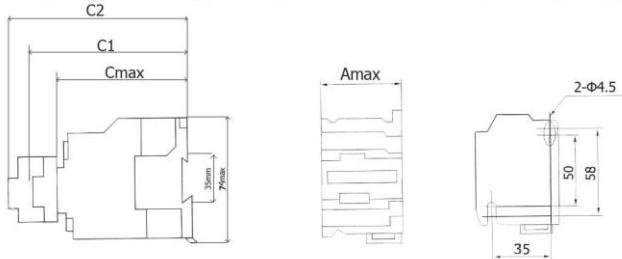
Габаритные и присоединительные размеры пускателей 16-40А
